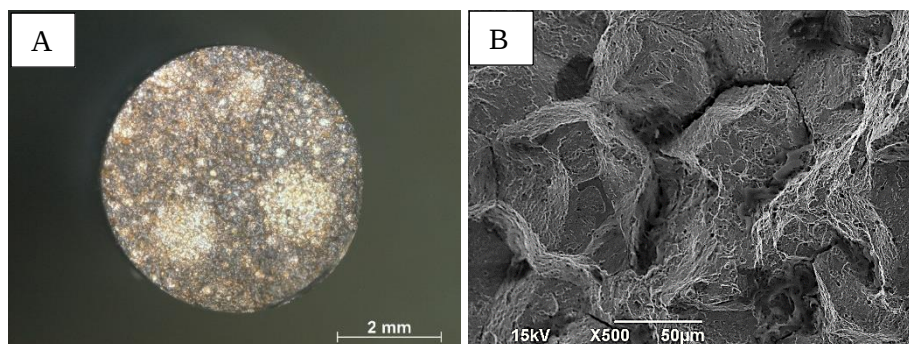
Superfície de fratura frágil (esquerda). Mecanismo de fratura intergranular (direita).
